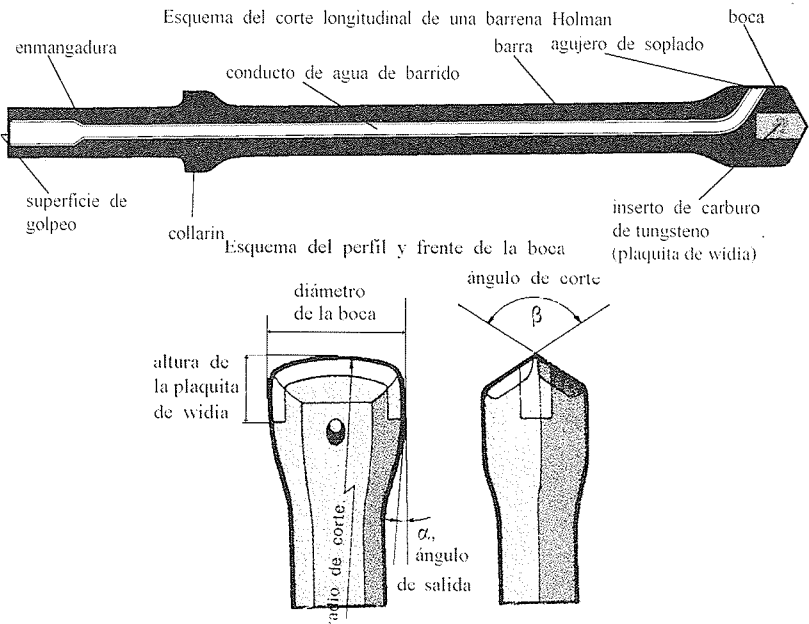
Detalle del interior de una barrena y su sección de corte
